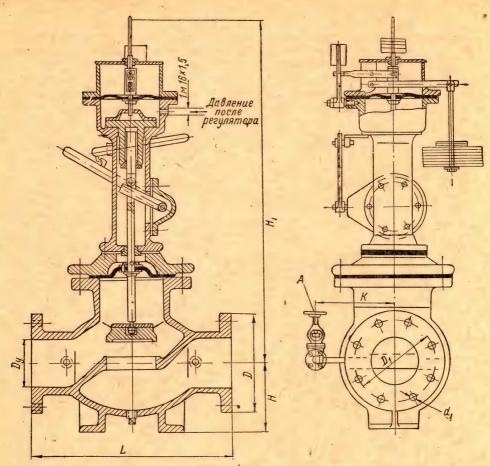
Предохранительный запорный клапан типа ПК-150, ПК-200 и ПК-300: A — вентиль обвода клапана.
